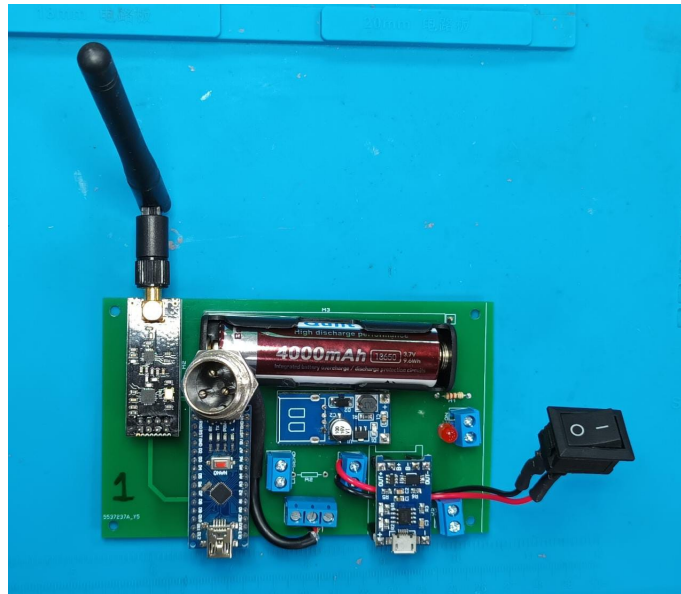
Montaje de componentes en PCB de un nodo sensor.
